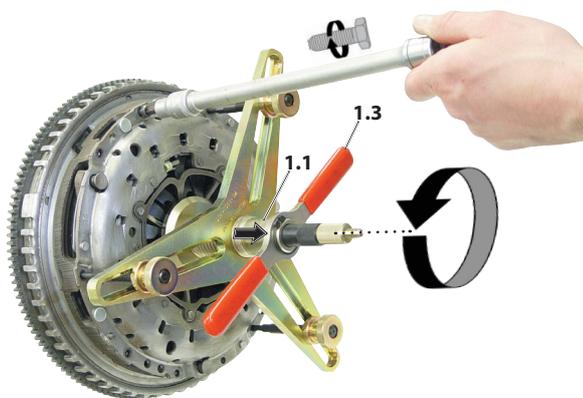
Alle Teile des SAC-Werkzeuges abbauen und entfernen.
